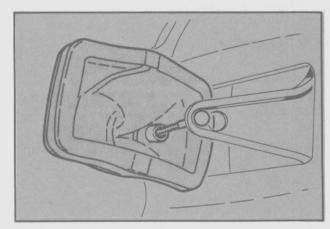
Desmontaje del guardapolvo de la horquilla de desembraque.
